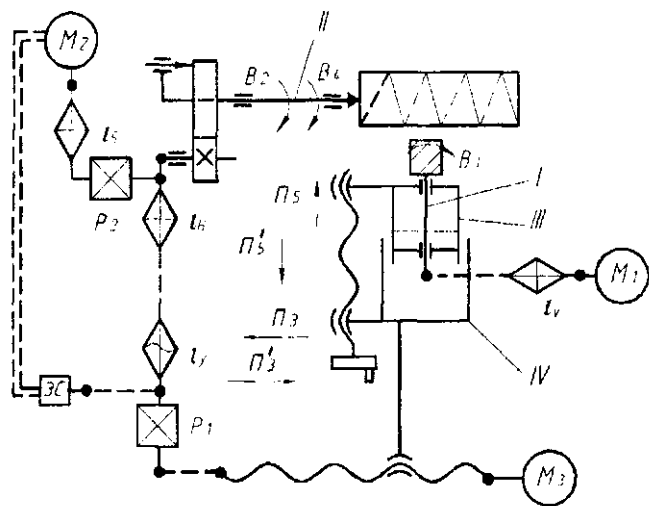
Структурная схема станка для фрезерования винтовых канавок переменного шага
